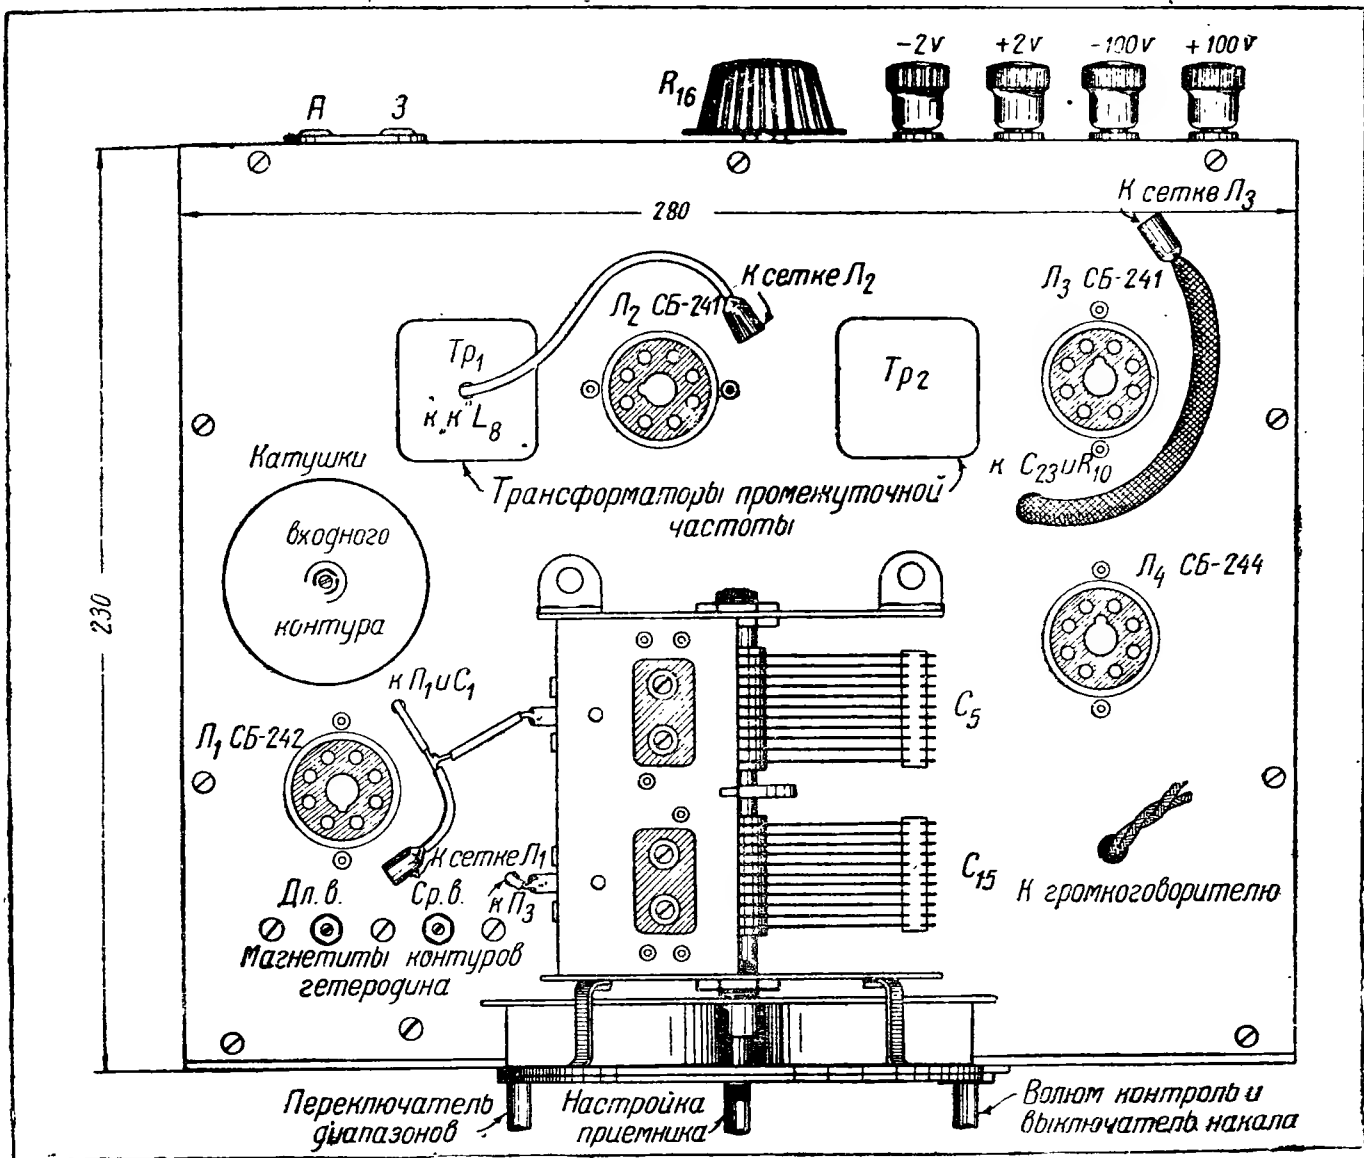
Расположение деталей сверху шасси батарейного приемника
